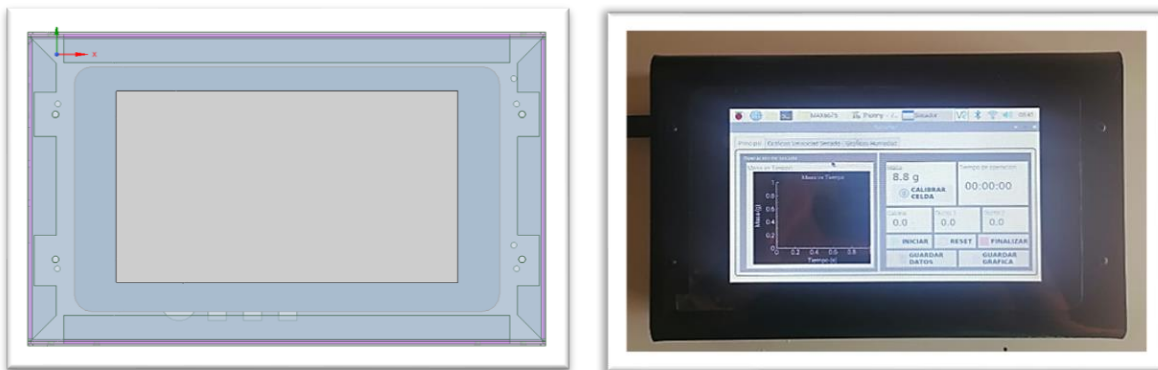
Diseño y ensamble de la caja del módulo parte frontal
